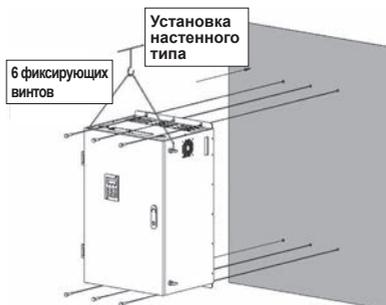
д Установка настенного типа в металлическом корпусе
